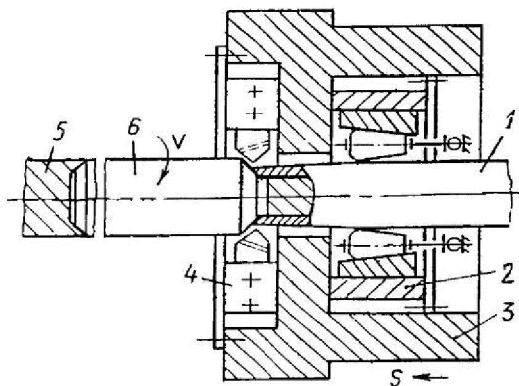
Комбинированный режуще-деформирующий инструмент для обработки нежестких валов
